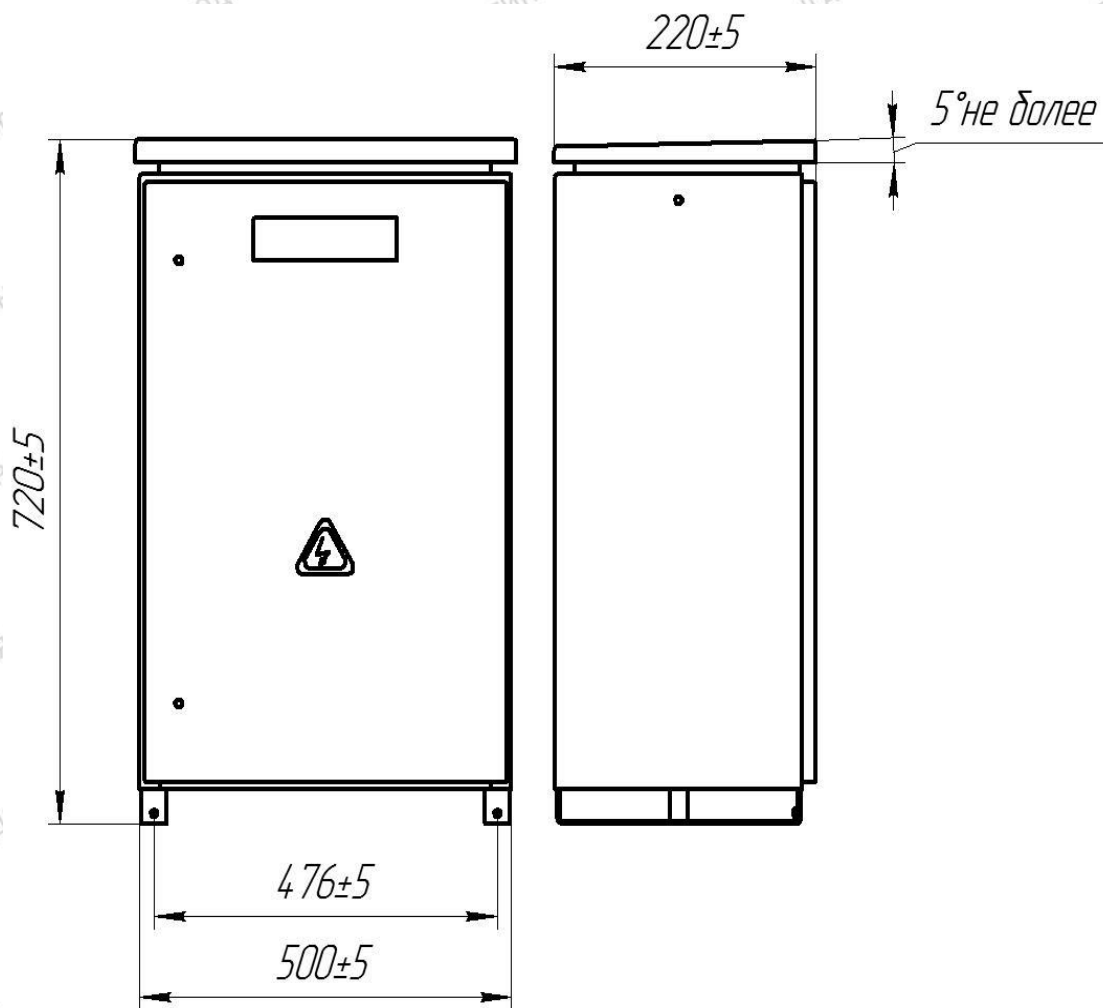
Общий вид и габаритные размеры БАР в исполнении У1
